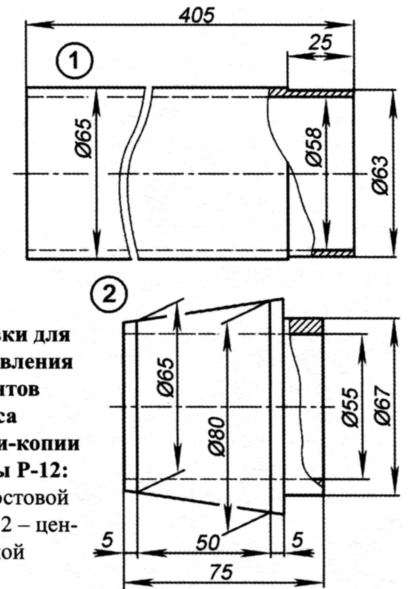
Оправки для изготовления элементов корпуса модели-копии ракеты Р-12:
